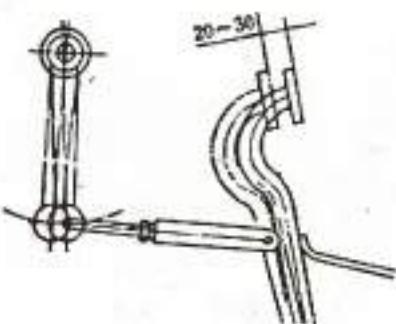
3 Регулировка свободного хода педали муфты сцепления
